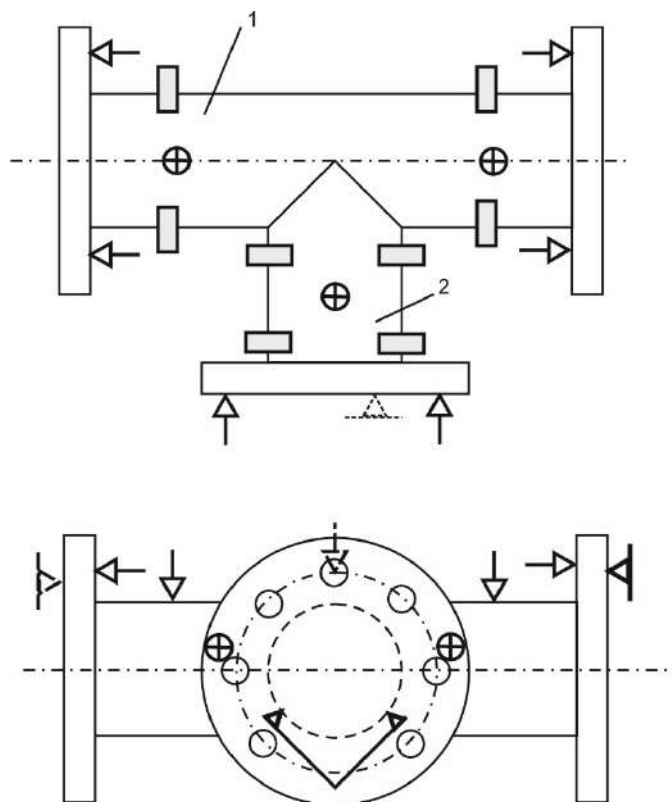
Принципова схема розміщення елементів базування та закріплення деталей патрубка при зварюванні
